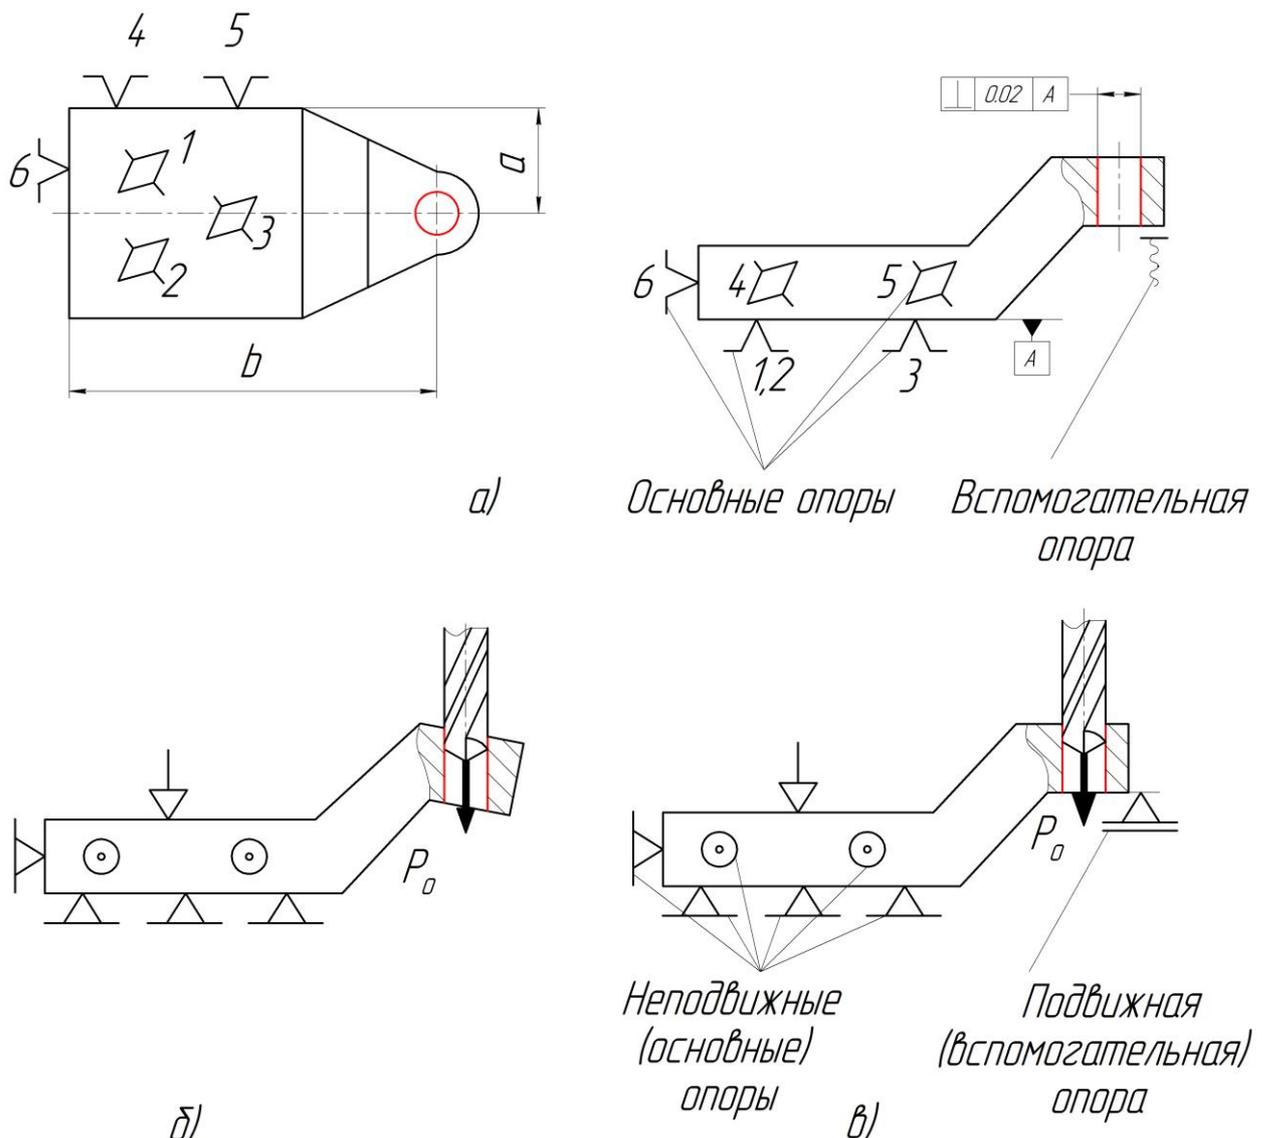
Схемы установки заготовки на операции сверления отверстия:
